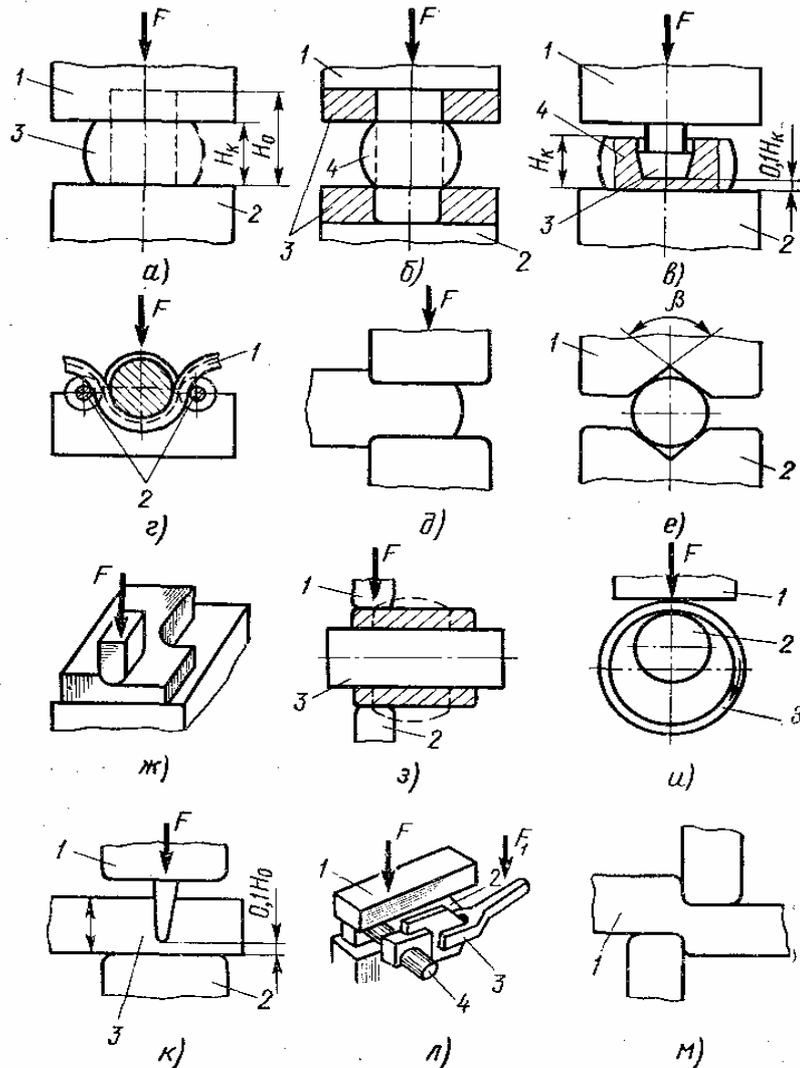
Схемы основных операций свободной ковки: а – осадка; б – высадка; в – прошивка; г – гибка; д,е,з – протяжка; ж – разгонка; и – раскатка; к – рубка; л – скручивание
